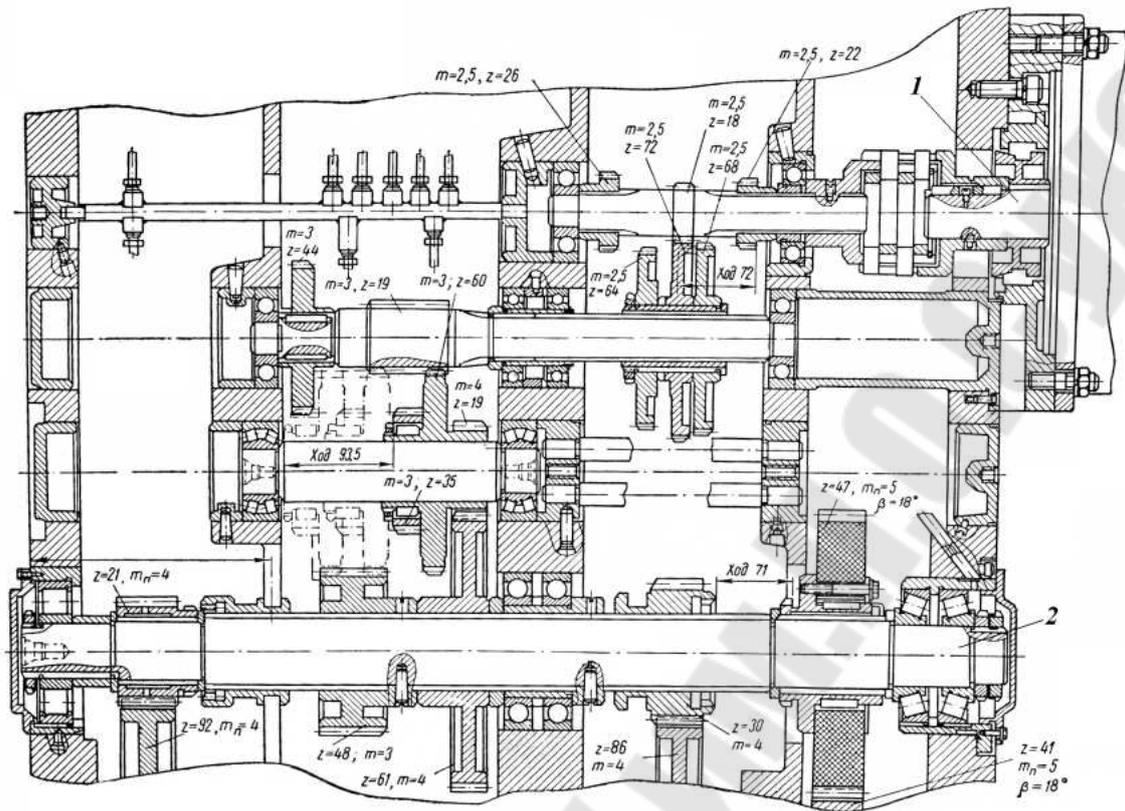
Коробка скоростей расточного станка 2620:
